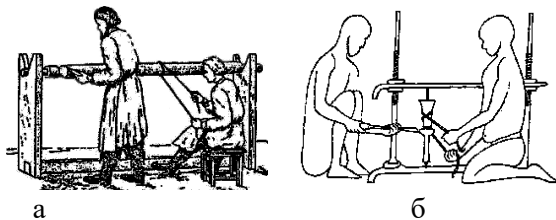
Перші токарні пристрої з ручним приводом
